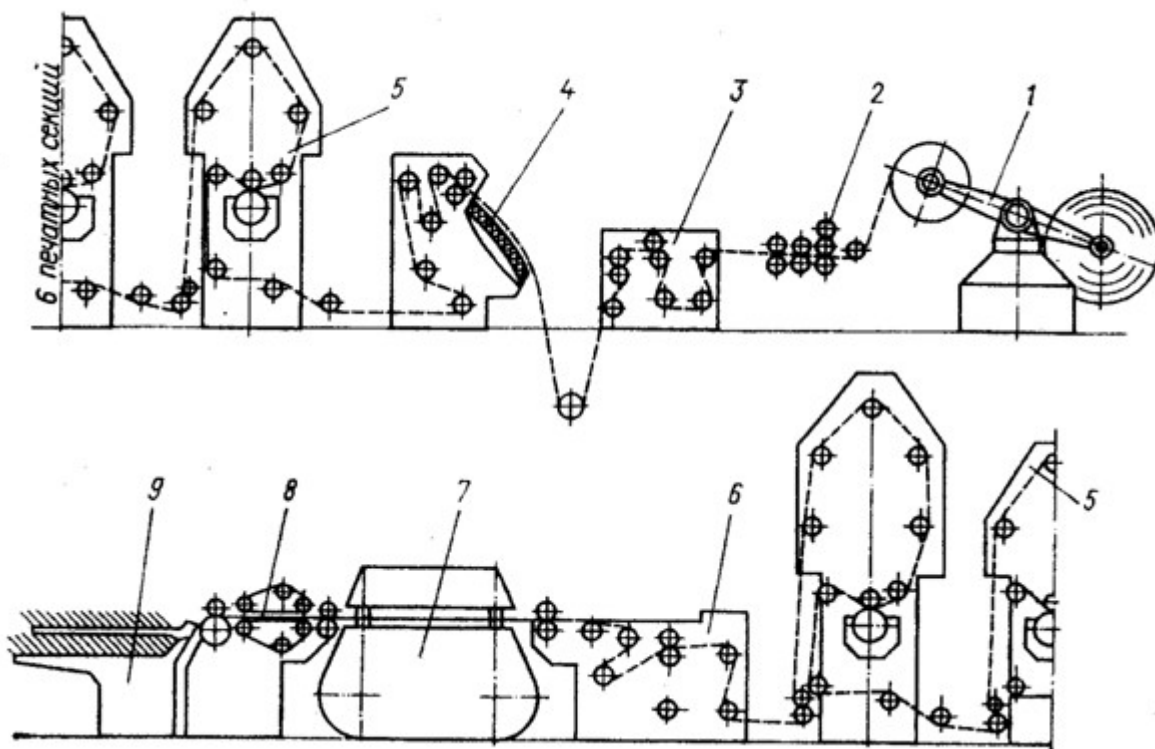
Схема высекательного автомата «Бобст-Чемплейн» марки А-25/С-42: 1 – стойка для рулонов; 2 – узел для сращивания полотна картона; 3 – тянущее устройство; 4 – накладное устройство; 5 – печатный аппарат; 6 – коробка передач для точной регулировки; 7 – штанцевальный аппарат; 8 – вырывающее устройство ротационного типа; 9 – двойной выводящий стол узла выдачи готовых высечек изделия
